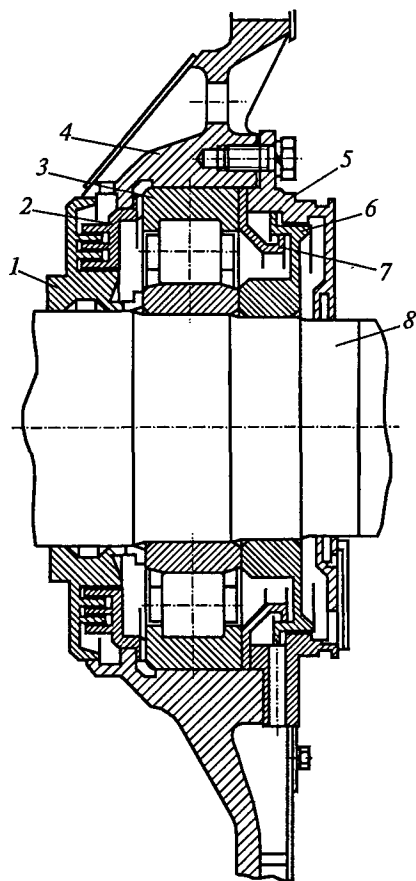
Большой подшипниковый щит электродвигателя ДТК-800КЭ:
